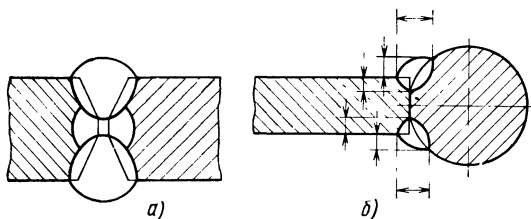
Условное обозначение сварного шва в разрезе (а) с размерами (б)
